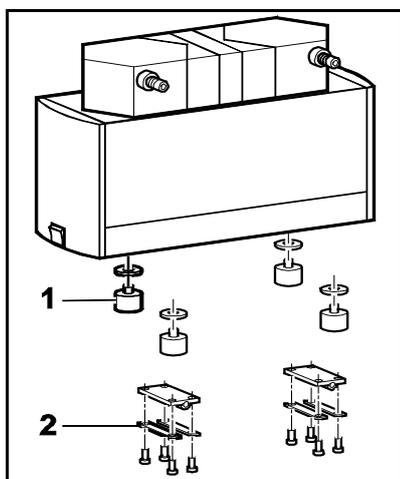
montaggio degli elementi di fissaggio sulla pompa
